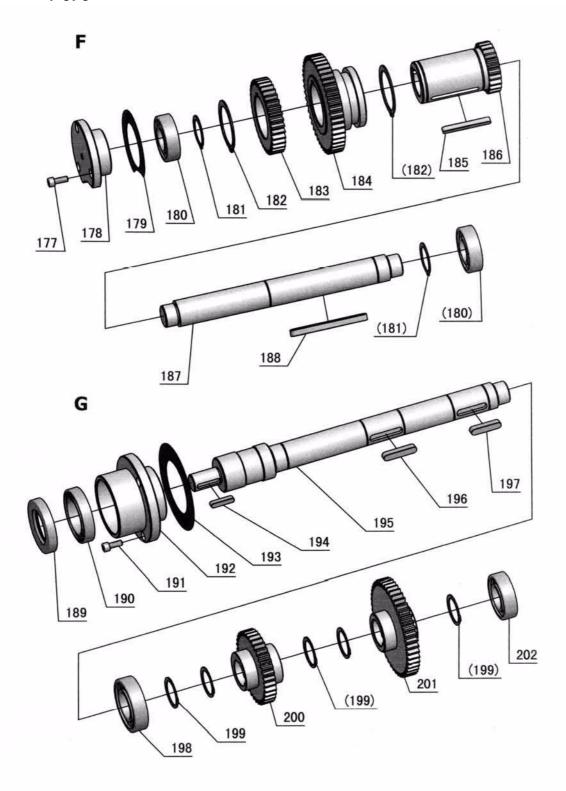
Spindelstock 7 von 8 - Headstock 7 of 8
